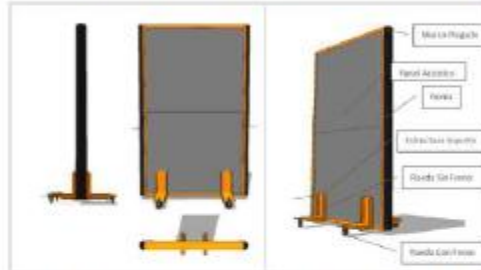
Vistas en: elevaciones y planta, además de vista en 3D indicando las partes que componen la barrera acústica móvil.
